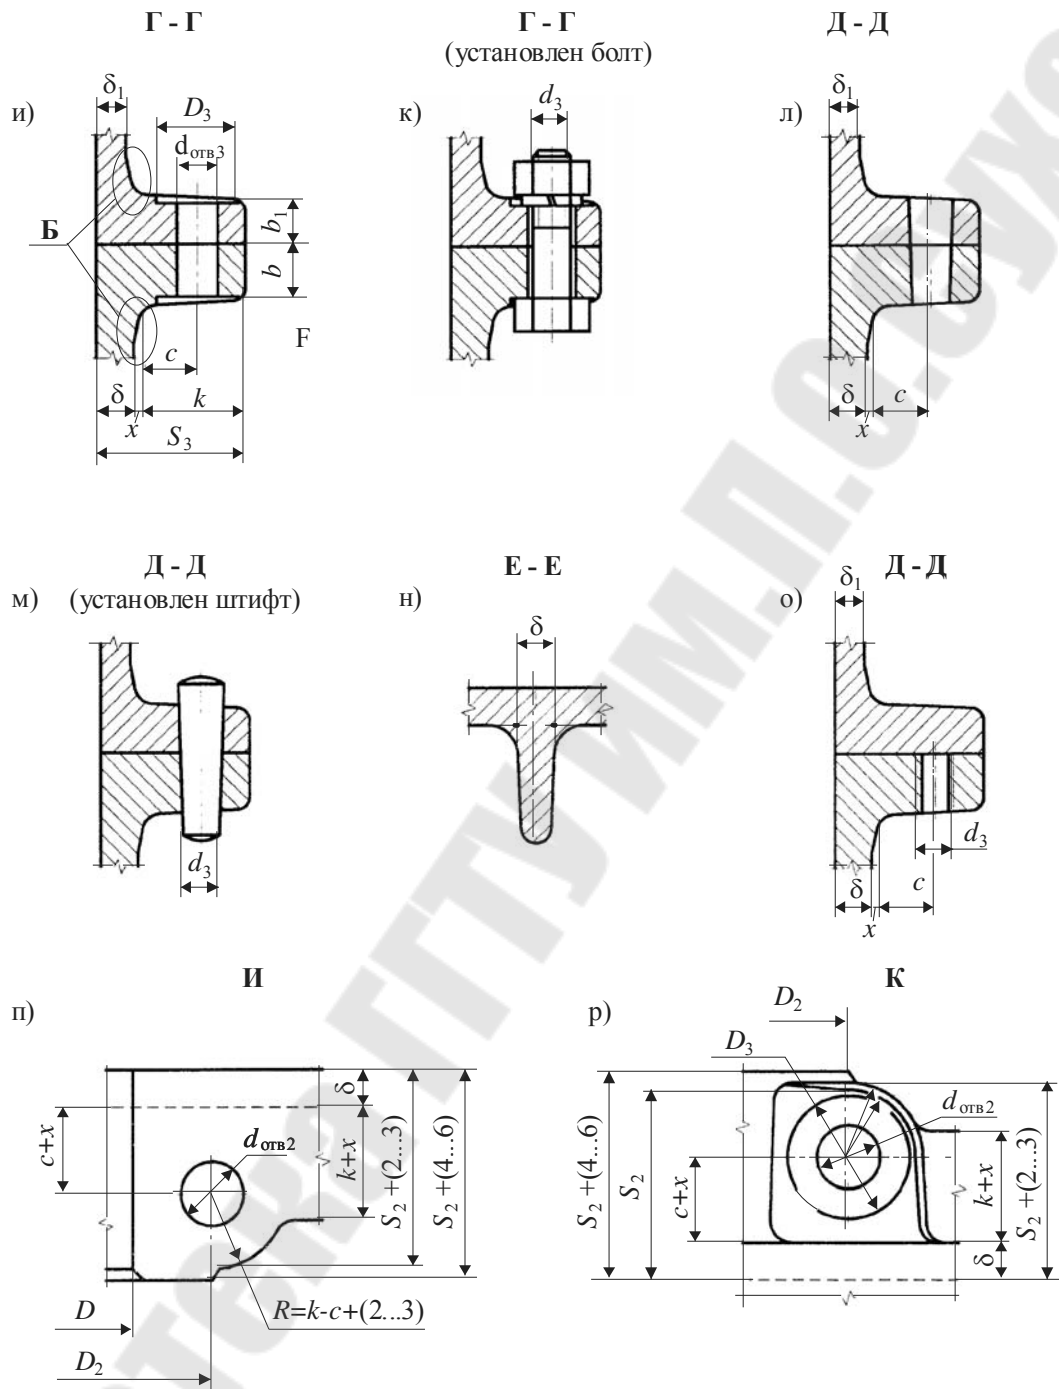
Элементы конструкции корпусных деталей редукторов с внешним расположением бобышек
